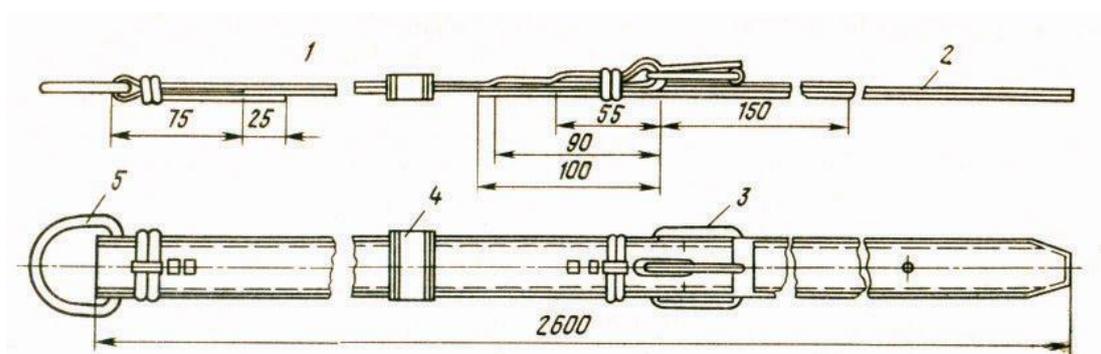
Нашильник сыромятный: 1 – ремень верхний; 2 – ремень подстрочный; 3 – накладка под пряжку; 4 – рамка; 5 – шлевка; 6 – пряжка шпеньковая.
